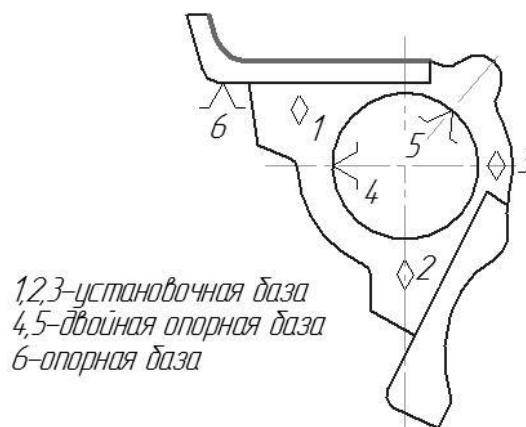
Схема базирования для фрезерной операции с ЧПУ №055
